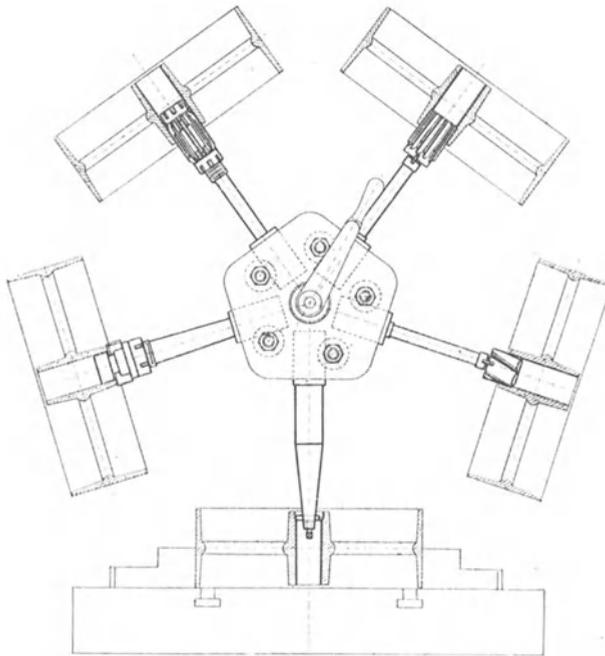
Bearbeitung der Bohrung auf einem Senkrecht-Bohr- und Drehwerk.
